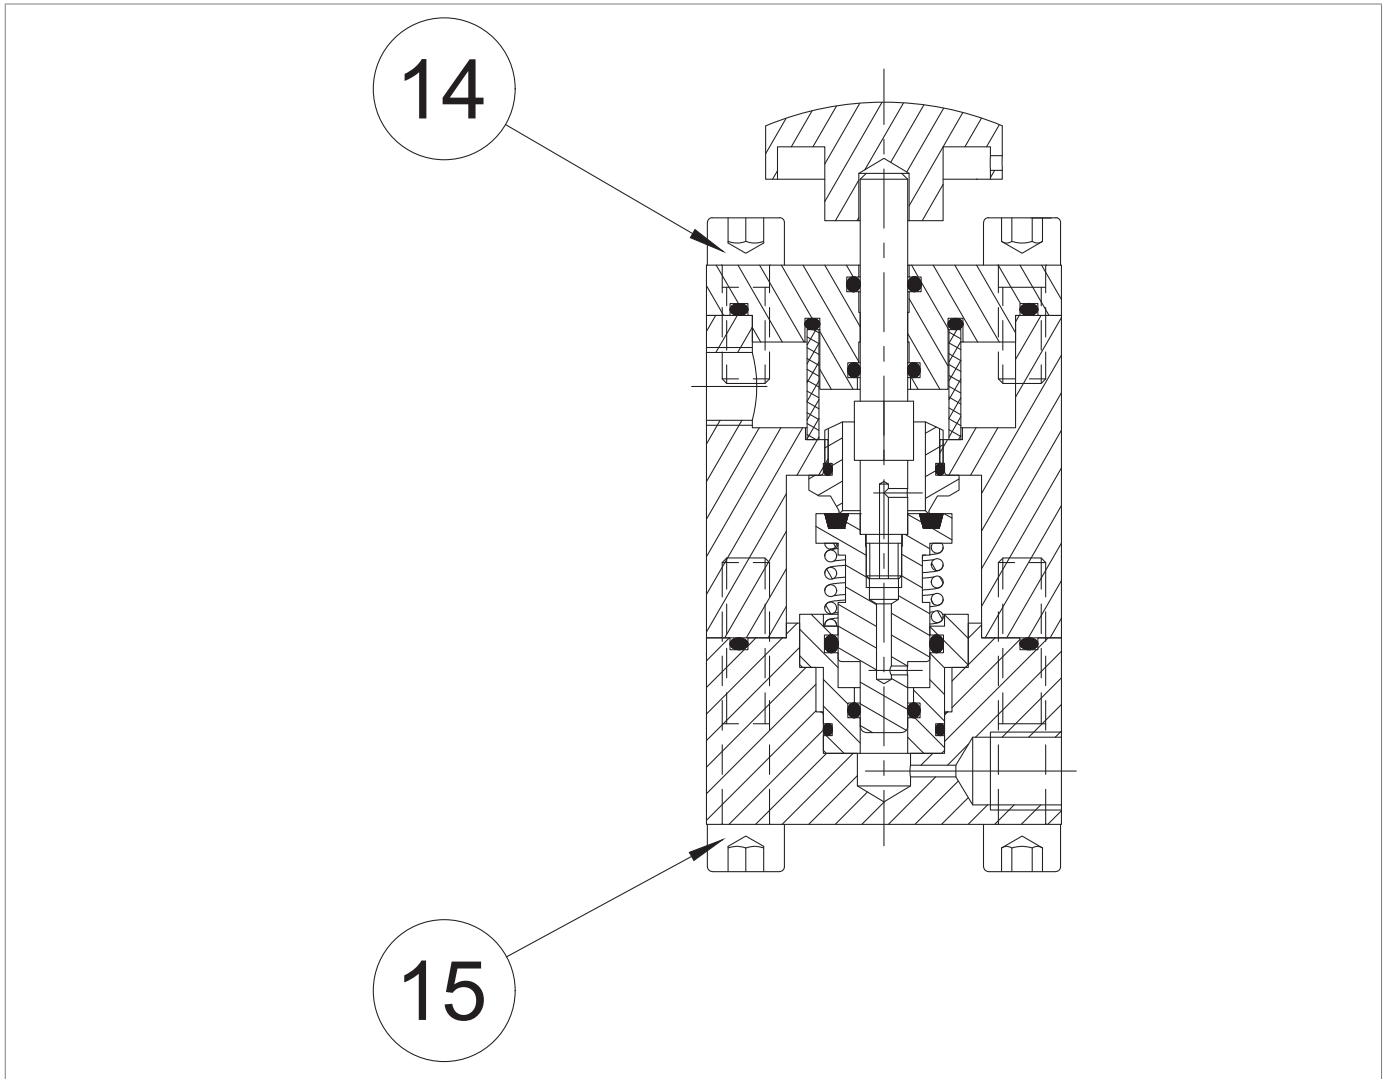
Pares de apriete del dispositivo bypass HP2/2
